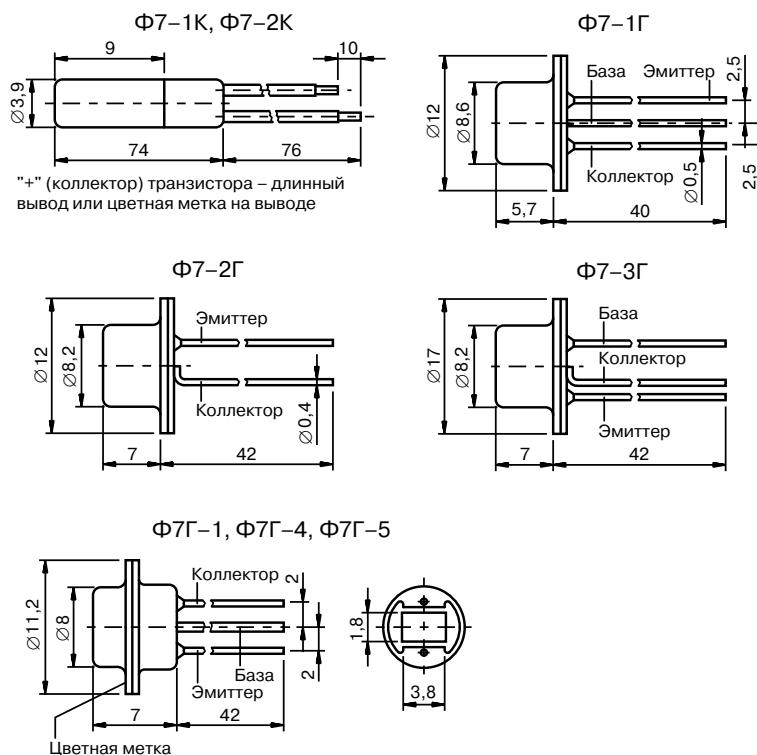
Внешний вид и габаритные размеры фототранзисторов
